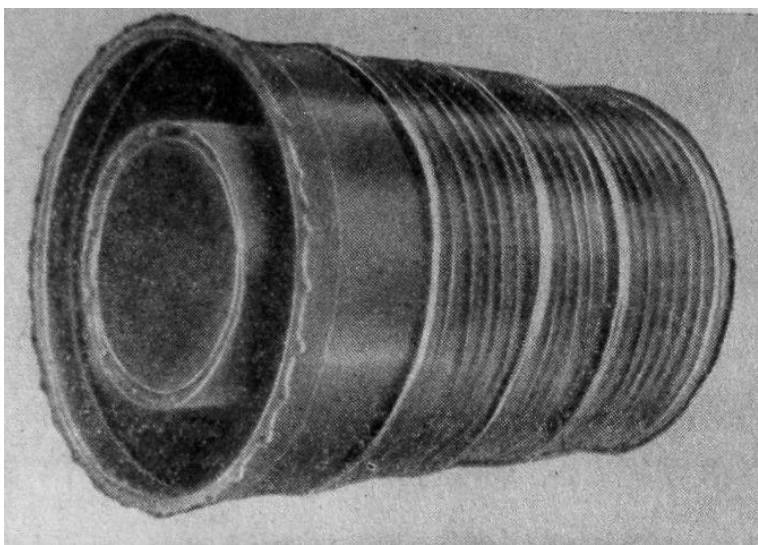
Реактивная труба со снятыми капотами и фольгой
